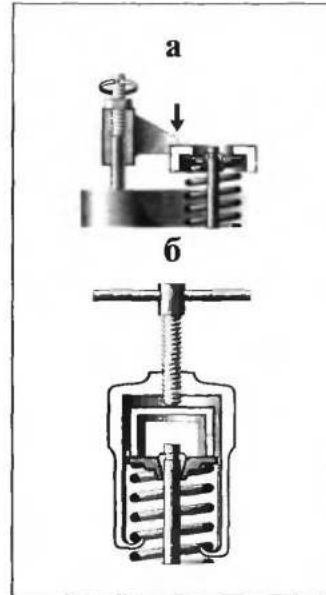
Винтовое приспособление для разборки/сборки клапанов: а — с опорой на технологическую шпильку; б — с захватом пружины клапана
